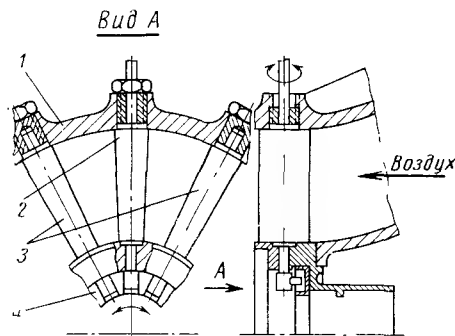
Поворотный направляющий аппарат компрессора ГТУ А-129 фирмы Блекборн:
